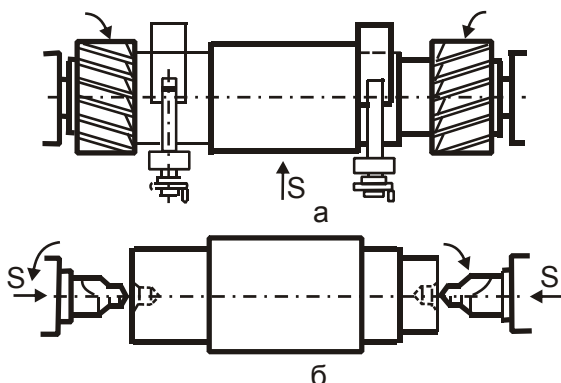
Схема обробки на фрезерно-центрувальному верстаті
